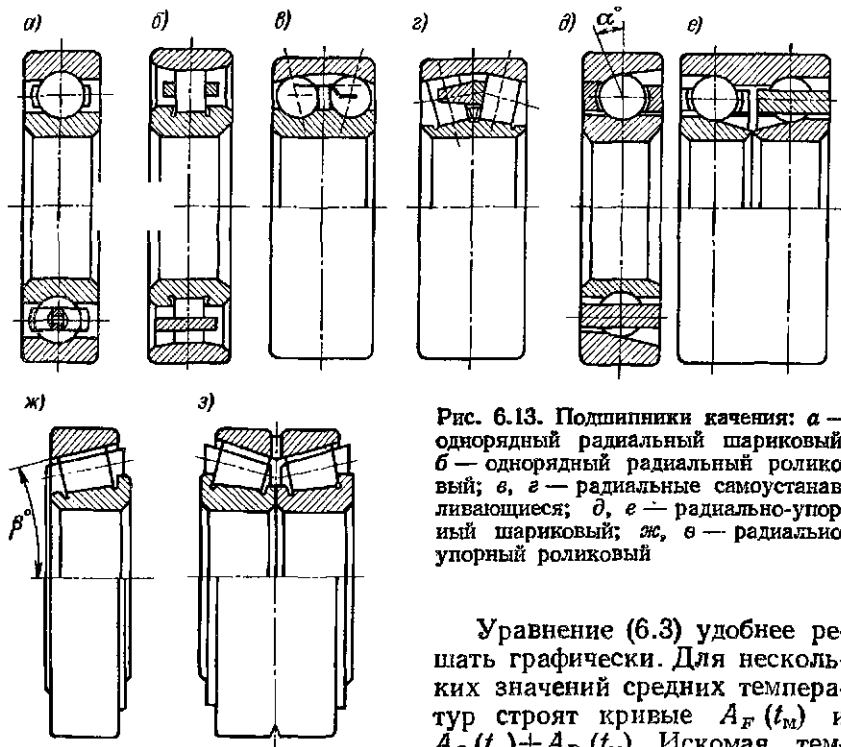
Подшипники качения: а — однорядный радиальный шариковый; б — однорядный радиальный роликовый; в, г — радиальные самоустанавливающиеся; д, е — радиально-упорный шариковый; ж, з — радиально-упорный роликовый
